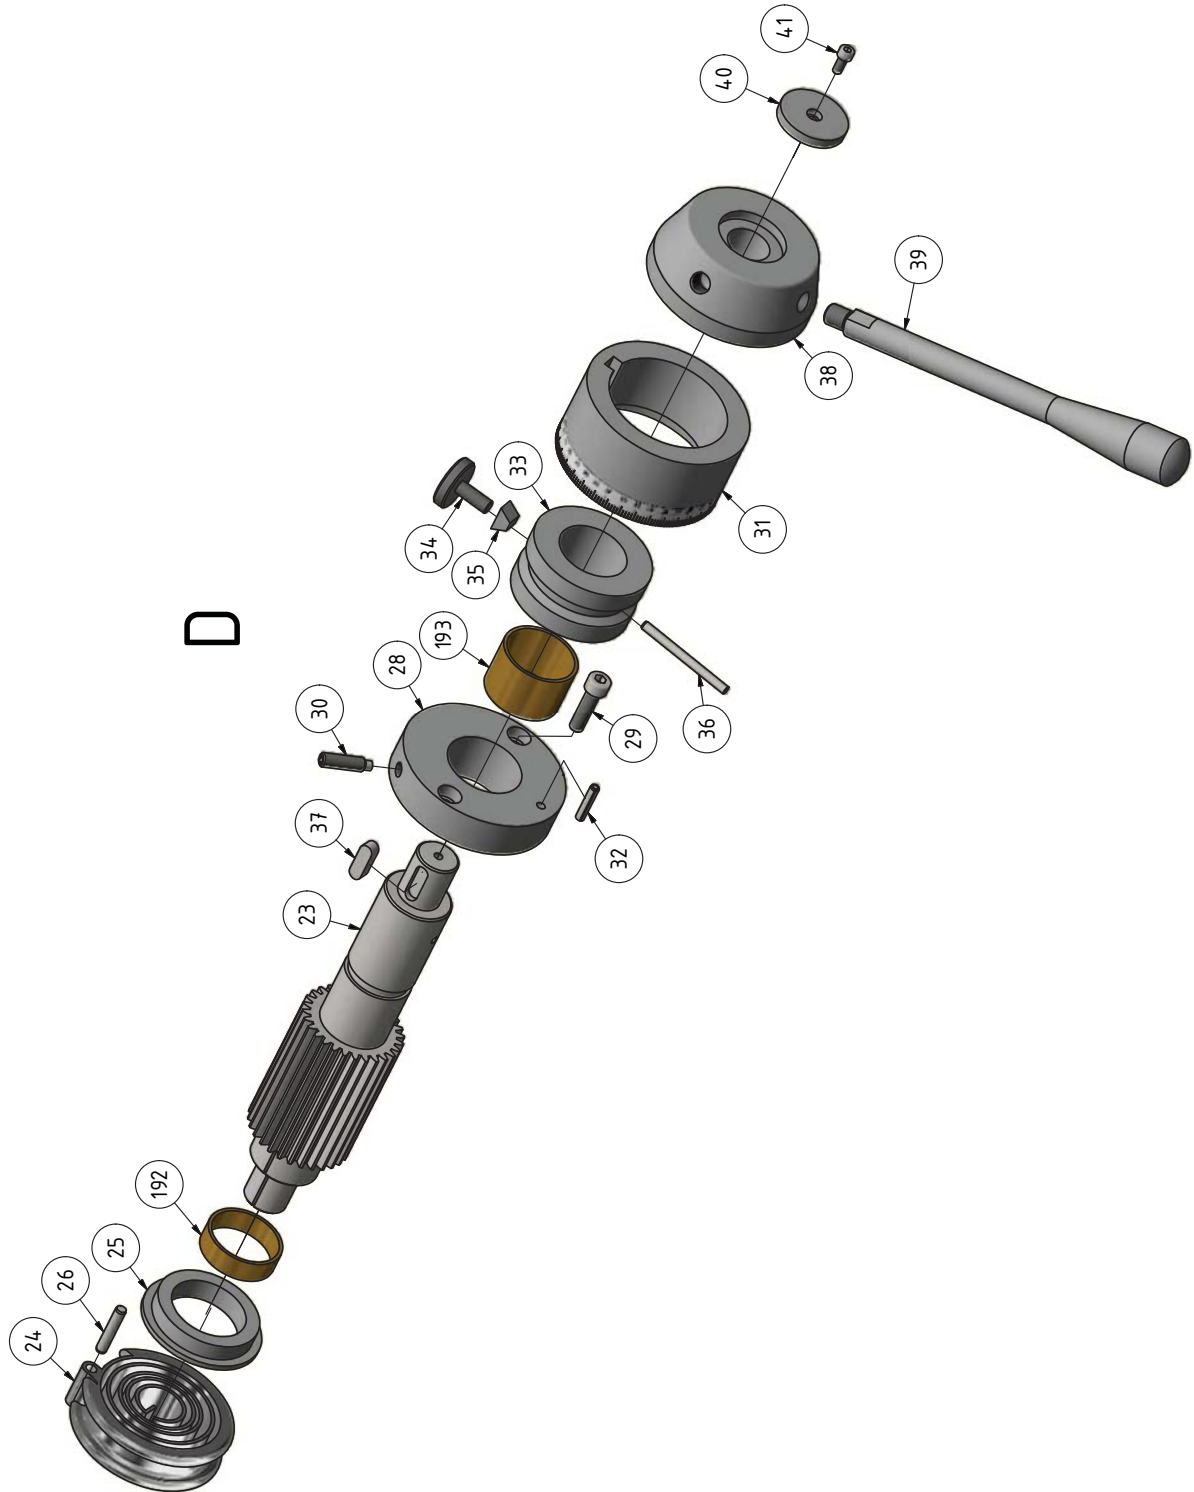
Bohrkopf 3 von 5 - Drilling head 3 of 5
